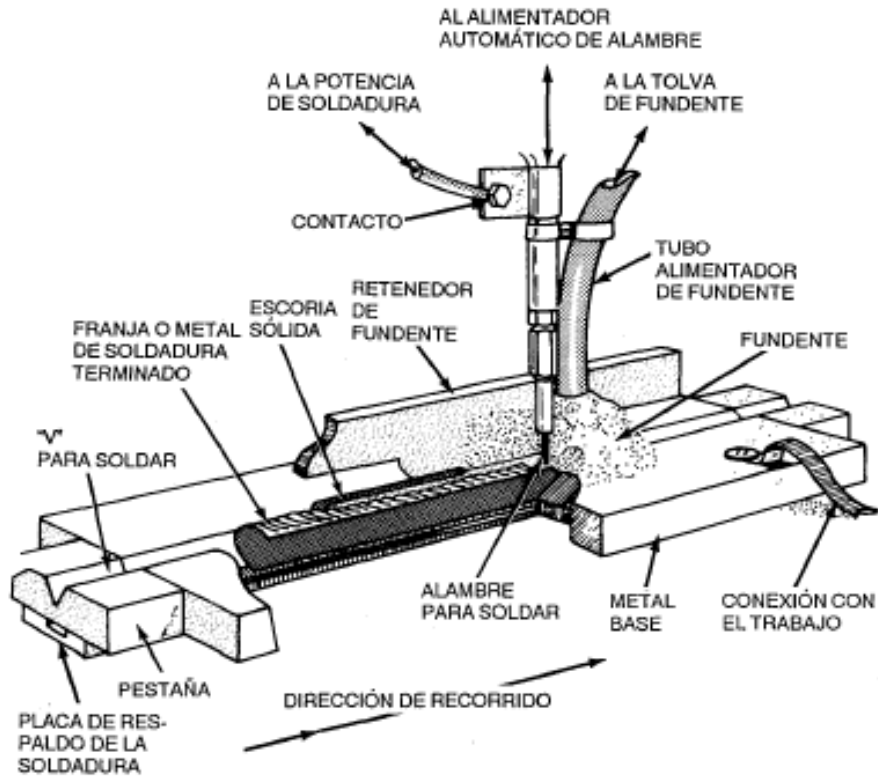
Esquema del proceso de soldadura por arco sumergido.
